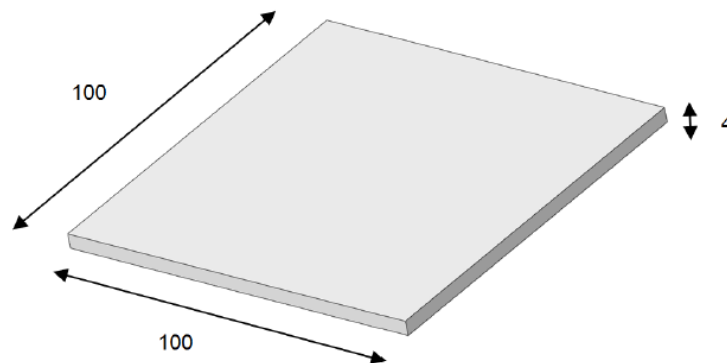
geometría y dimensiones de la placa de aluminio sobre la que se va a simular el impacto en mm.
